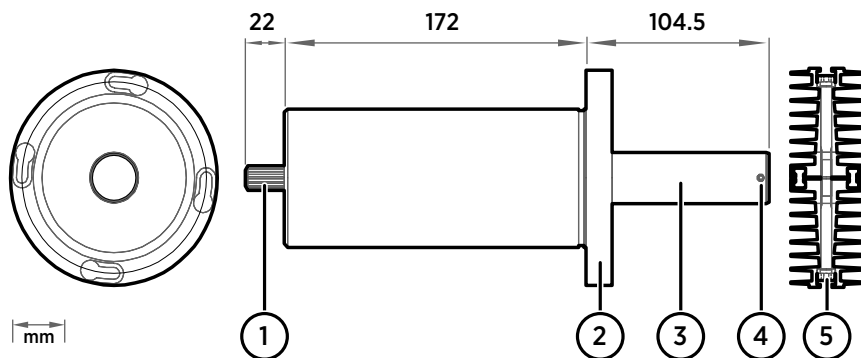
Conjunto de refrigeração DMP246CS sem flange de montagem
